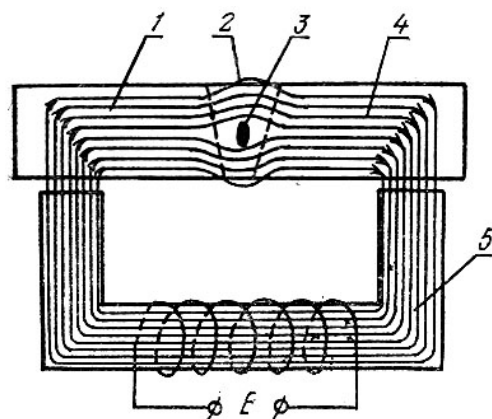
Магнитный поток в дефектном сварном шве:
